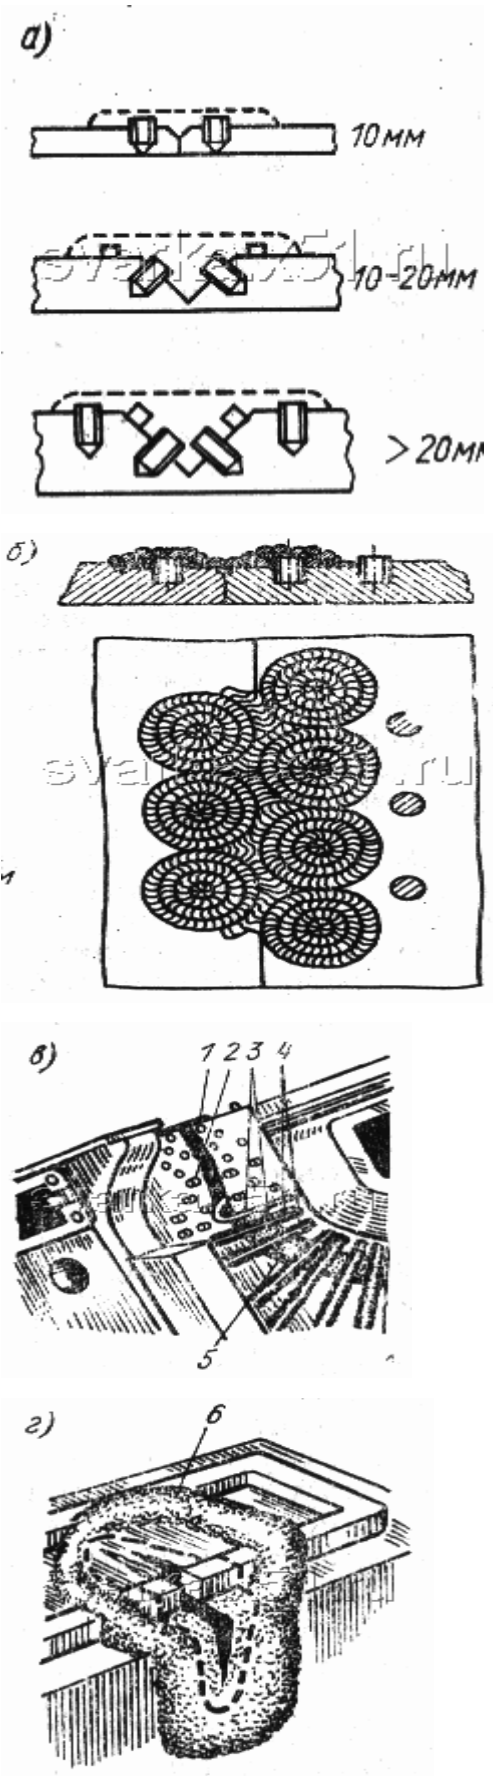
Сварка чугуна с применением стальных шпилек:
